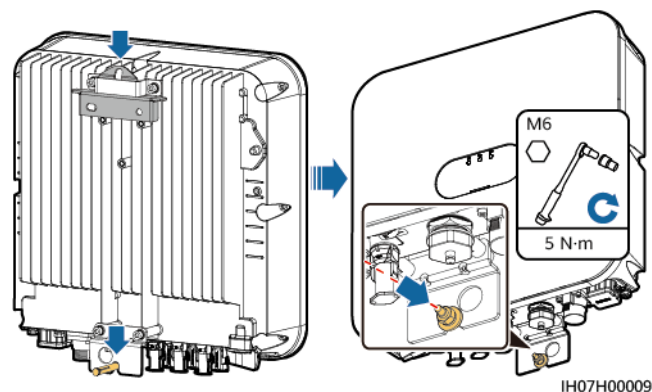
Instalação de um parafuso de travamento na DC switch
